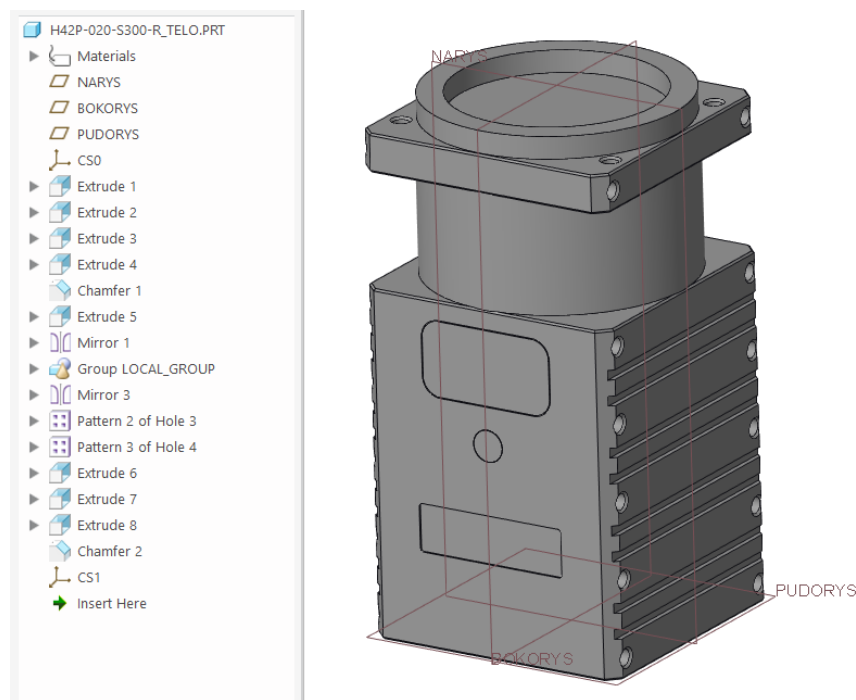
H42-P-020-S300-R\_telo – drážky a sražení
